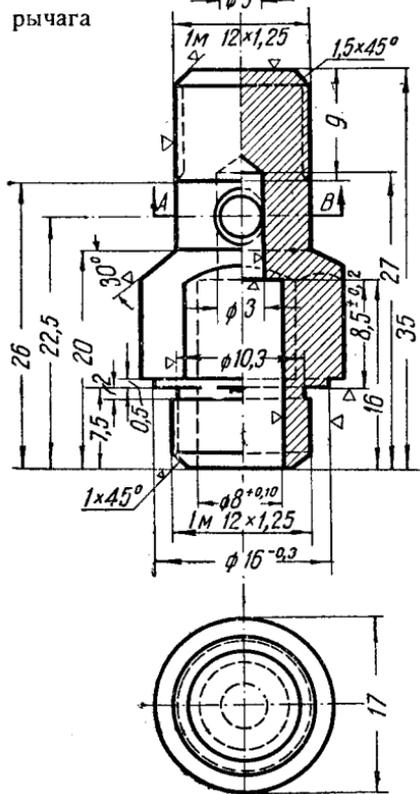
Дет. № 329. Корпус игольчатого клапана для воды и топлива
